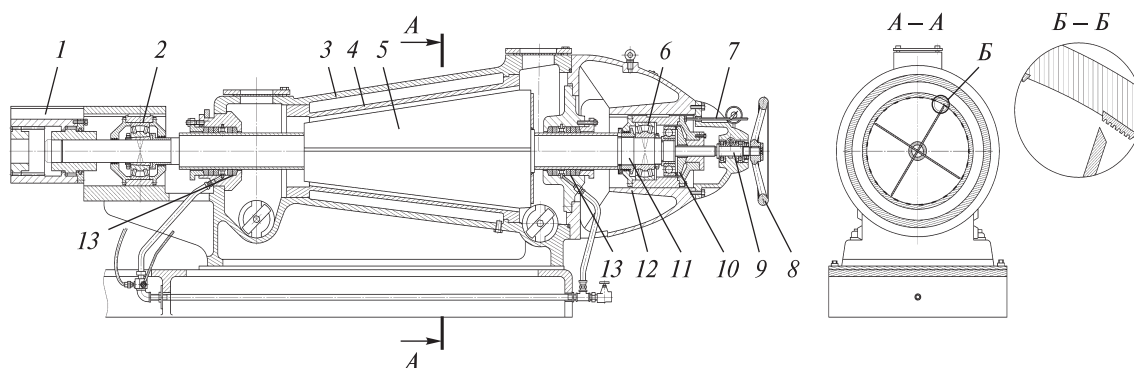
Схема размалывающей установки: 1 — соединительная муфта; 2 — задний подшипниковый узел; 3 — корпус; 4 — статор с закрепленными гребенчатыми планками; 5 — крестовина ротора; 6 — передний подшипниковый узел; 7 — контактная шпилька; 8 — штурвал регулировочный; 9 — регулирующий вал; 10 — крышка переднего подшипникового узла; 11 — вал; 12 — присадочный механизм; 13 — сальниковый узел
